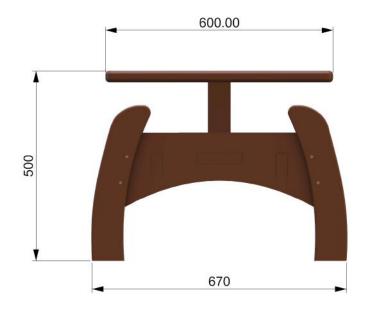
Dimensionamento geral - Mesa - Vista Lateral- Cotas em mm
